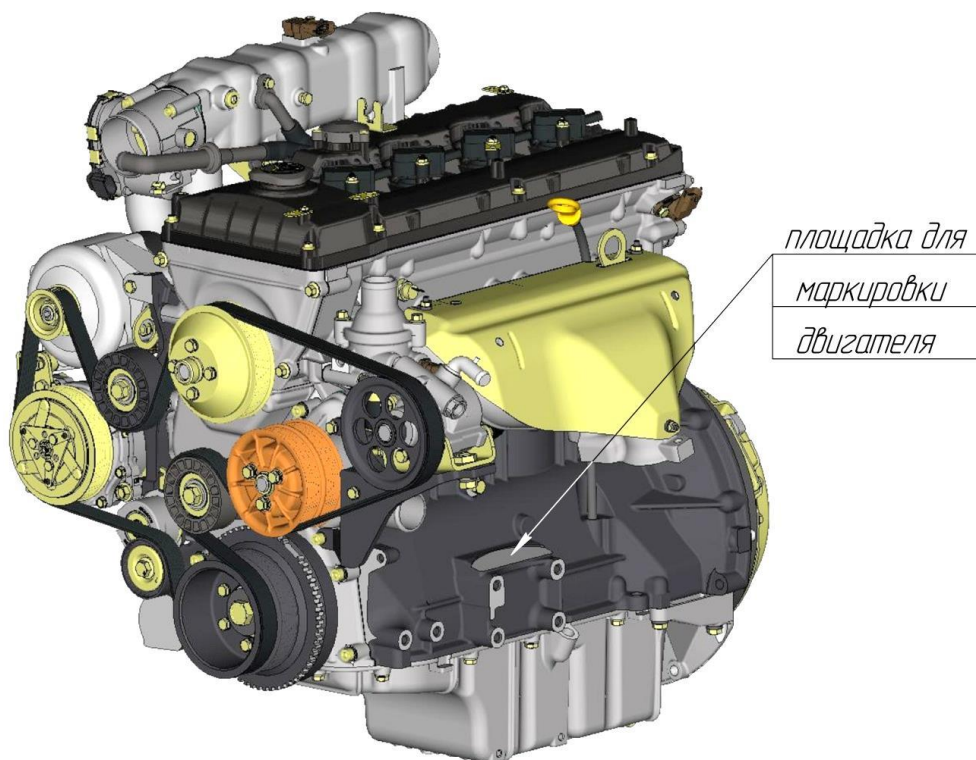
Общий вид двигателя ЗМЗ-40905.10
